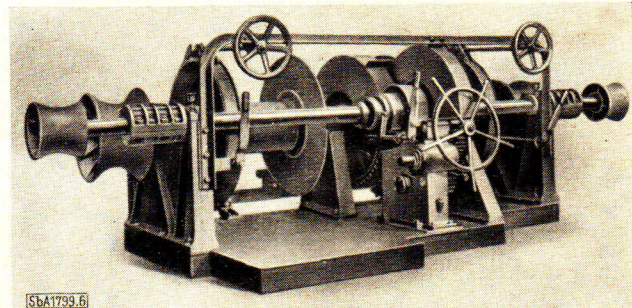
Fischnetzwinde 4 t ohne Motor und Außenlagerböcke für Vorgelegewelle
